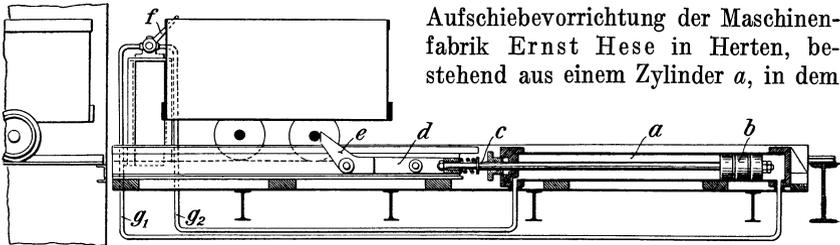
Aufschiebevorrichtung mit Preßluftzylinder.
